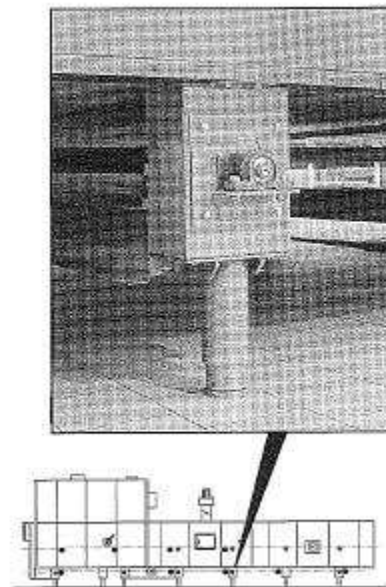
Parte inferior de un horno industrial, detalle de un rodillo y de su rodamiento.
